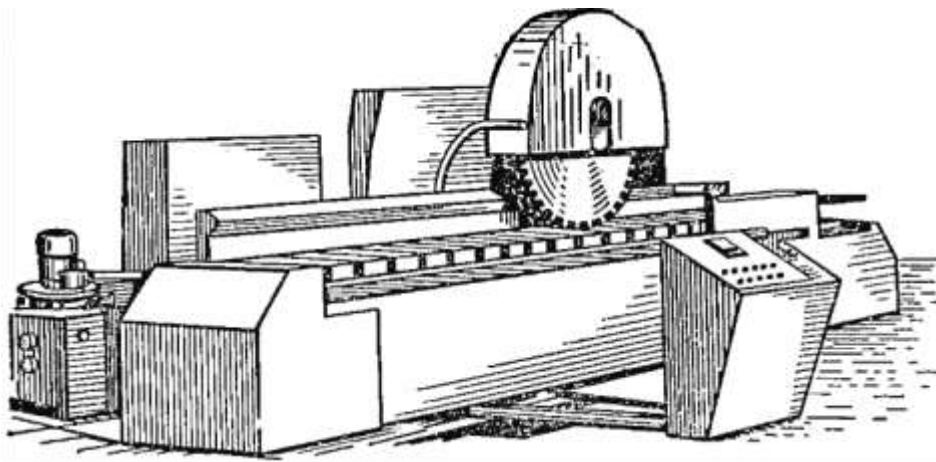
Багатодисковий одновальний семидисковий верстат СМР-056А [23].
